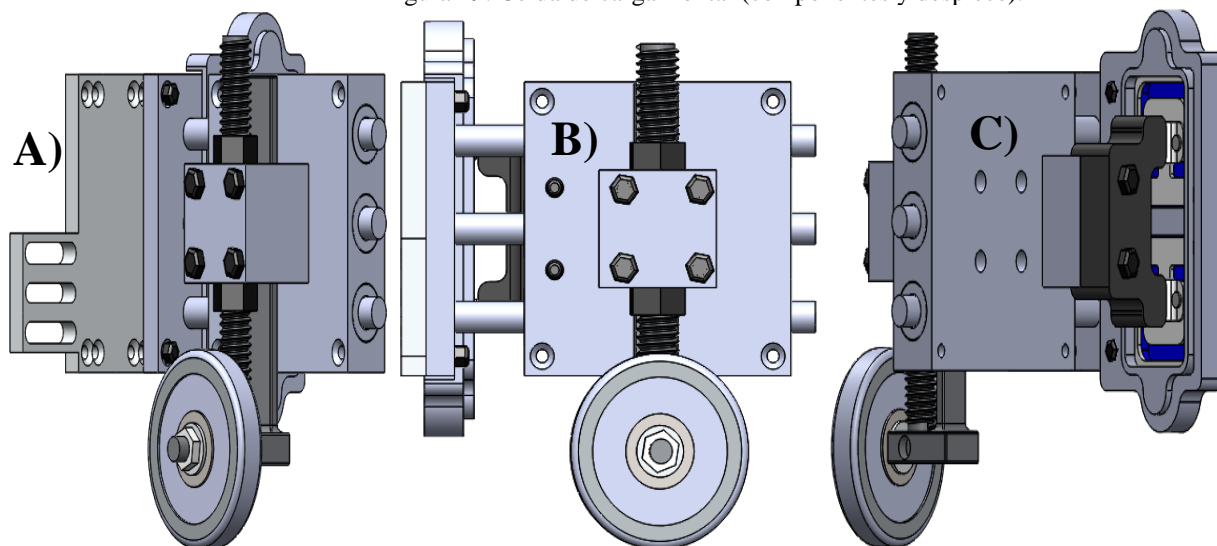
A) vista isométrica, B) vista lateral, C) vista isométrica derecha de la celda de carga frontal.
